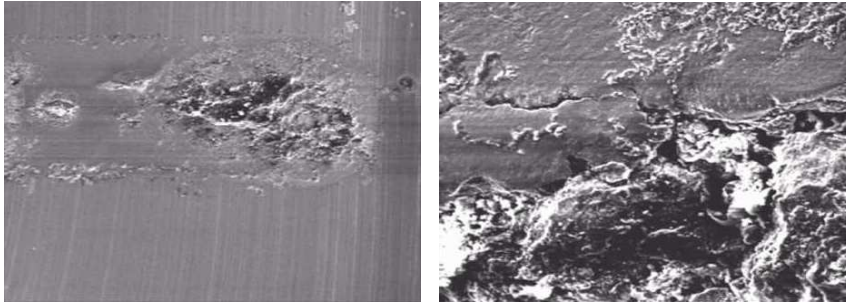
REM-Aufnahme aus [Tcho8], *links*: Riffelmarke in Laufbahn des Innenrings eines Wälzlagers, *rechts*: Detailansicht einer Riffelmarke mit verzweigten Rissen senkrecht zur Oberfläche
